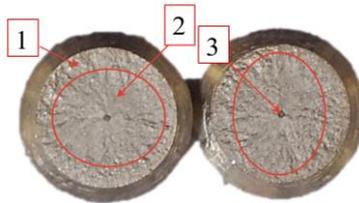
Образец стали класса прочности K60 после испытаний
